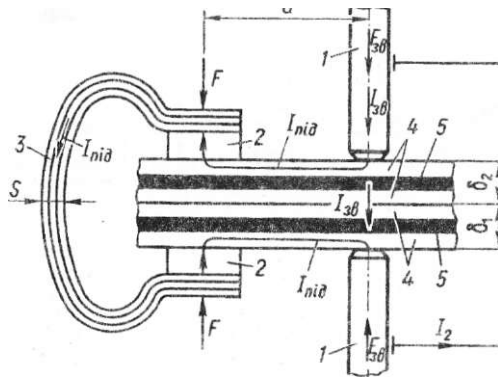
Принципова схема зварювання деталей із ШВМ:
